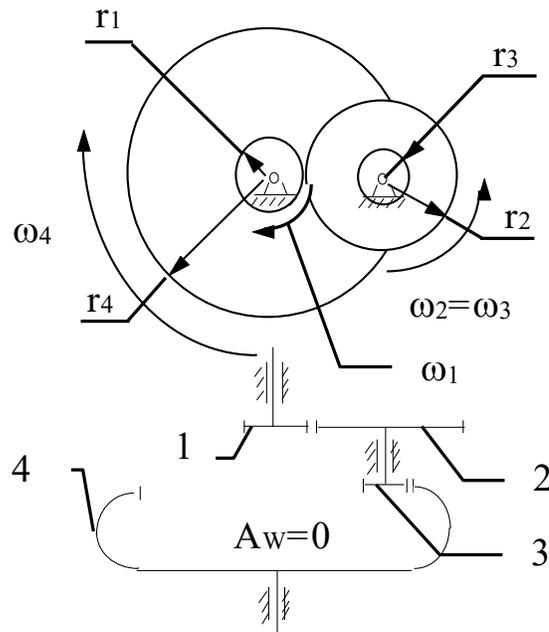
Кинематическая схема сложной зубчатой передачи с внешним и внутренним зацеплениями
